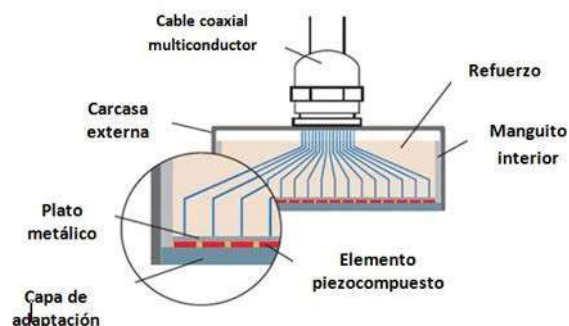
Corte-sección del Palpador de Arreglo de Fases.
